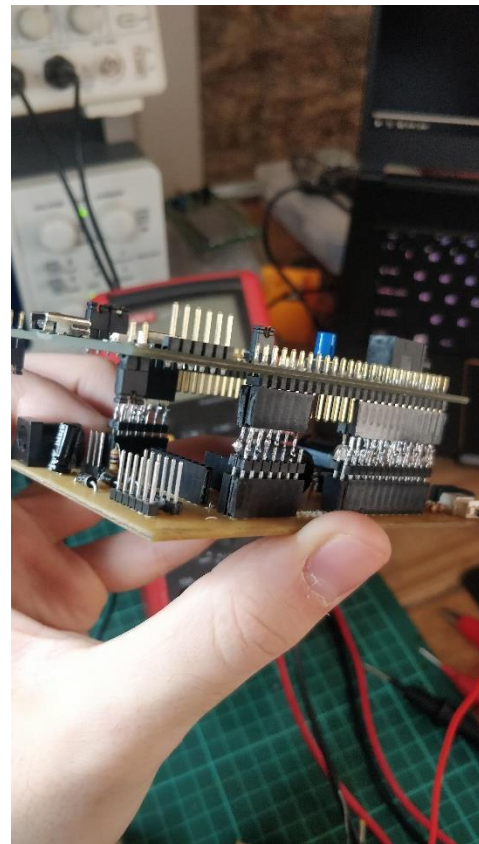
PCB Terminado y conectado a placa de desarrollo
